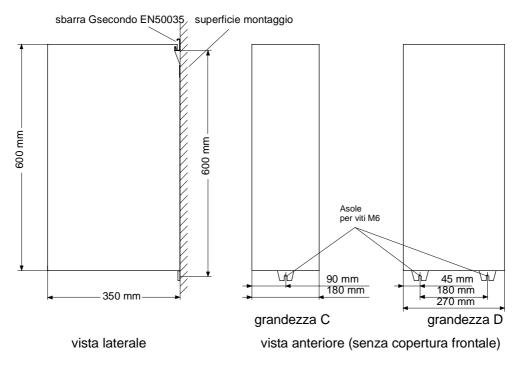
Disegni d'ingombro per montaggio grandezze C, D
